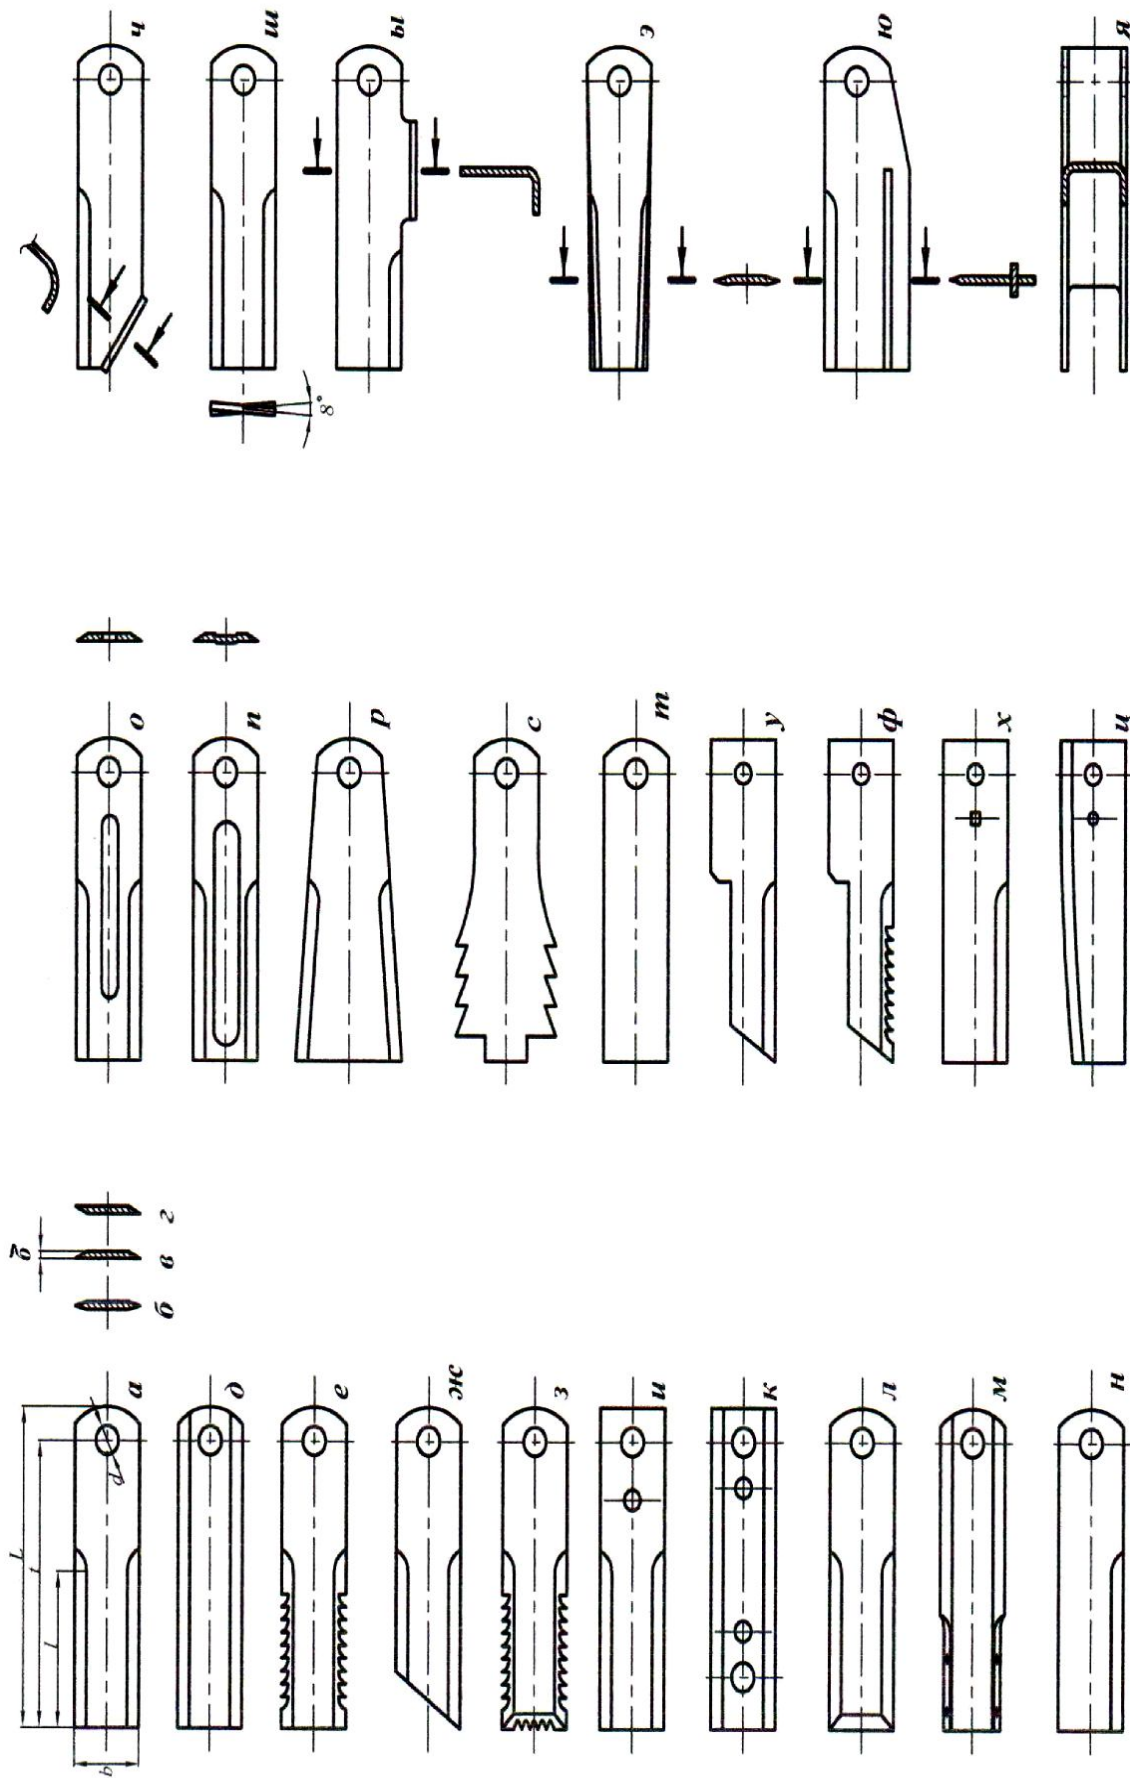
Типы ножей измельчителей-разбрасывателей зерноуборочных комбайнов
